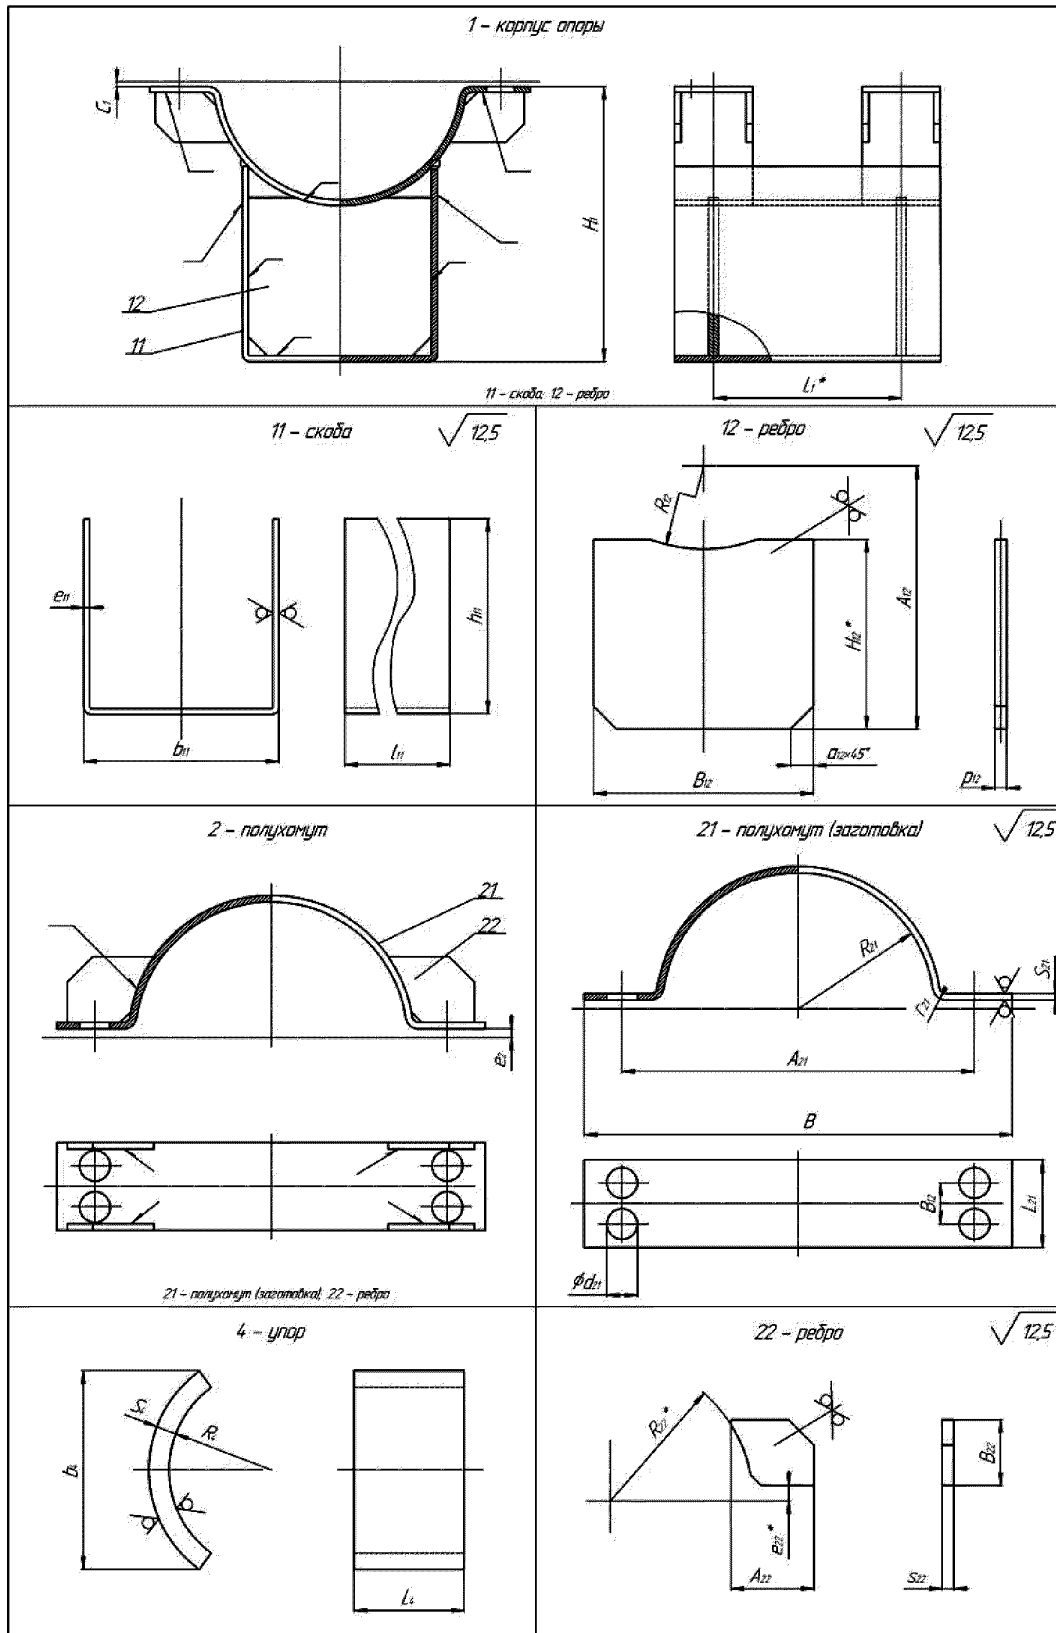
Детали изделий 01-XXXX-F-1С-03-А,
